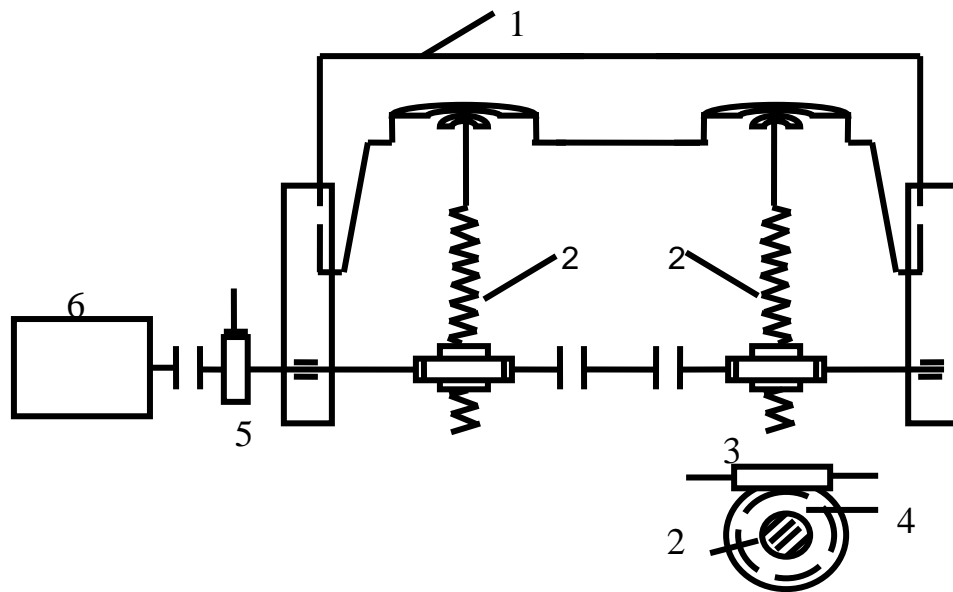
Кинематическая схема штабелирующего стола: 1 – подъемный стол; 2 – винты; 3 – червяк; 4 – червячное колесо; 5 – тормоз; 6 - двигатель
